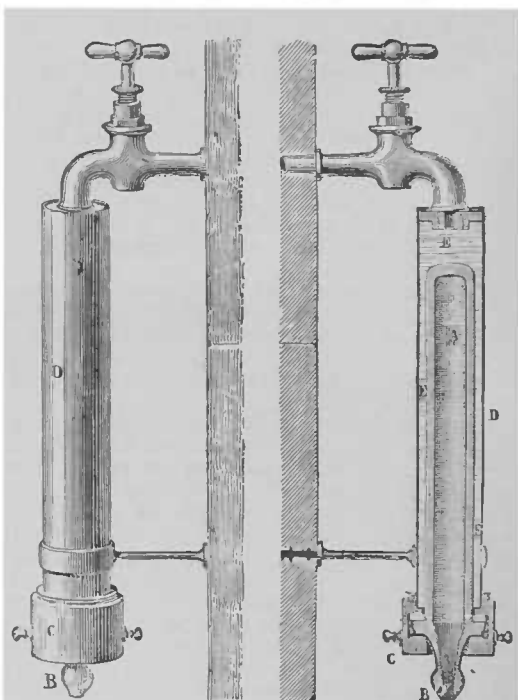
Filtre Chamberland pour stériliser l'eau de boisson (vue et coupe).
